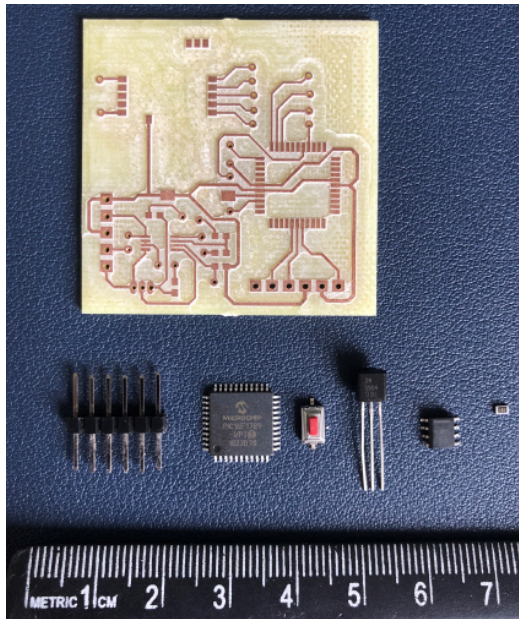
Dimensiones y componentes del prototipo final anterior [5].
